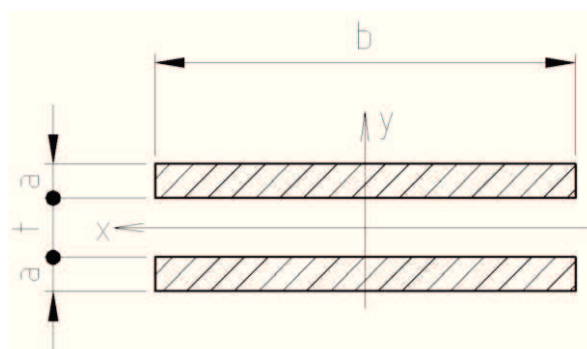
Svarový spoj č. 1 (úchyt pro zadní část motoru č. 1)
